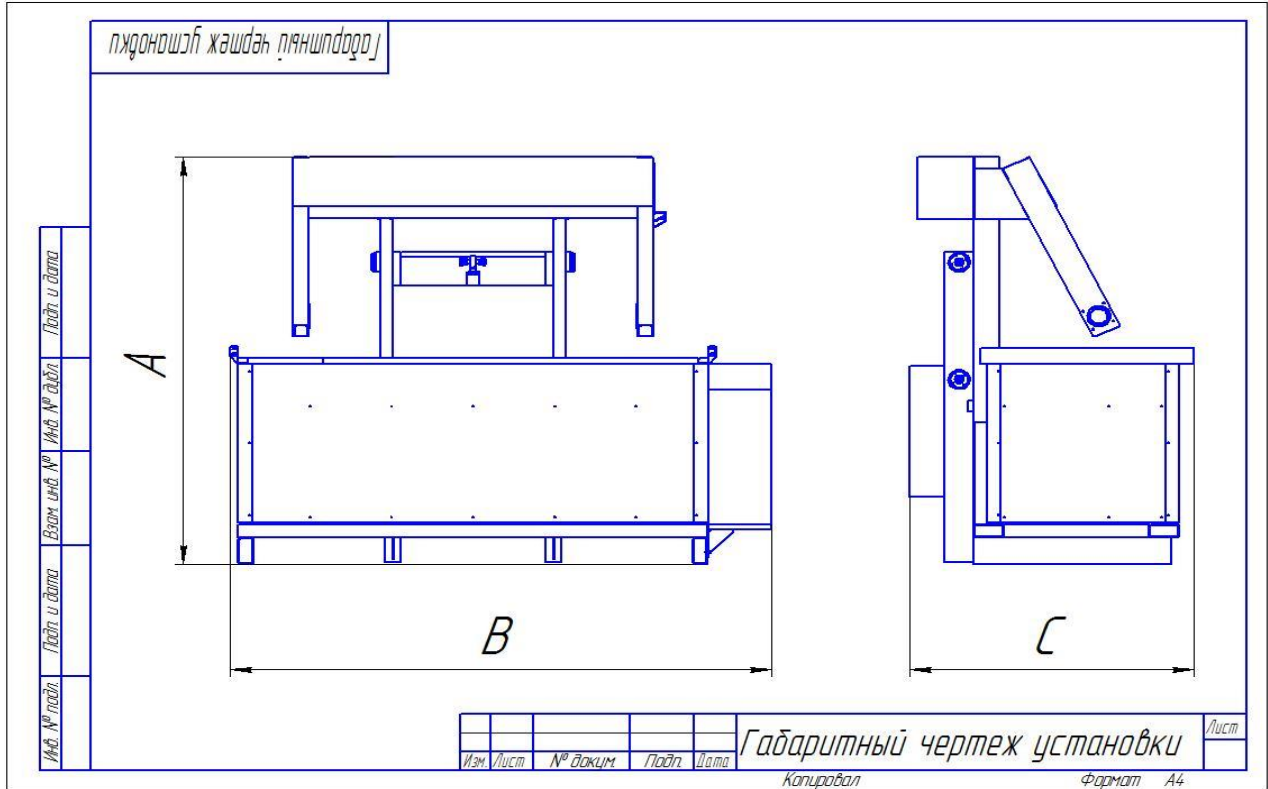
а. Габаритный чертеж установки с поднятым суппортом
